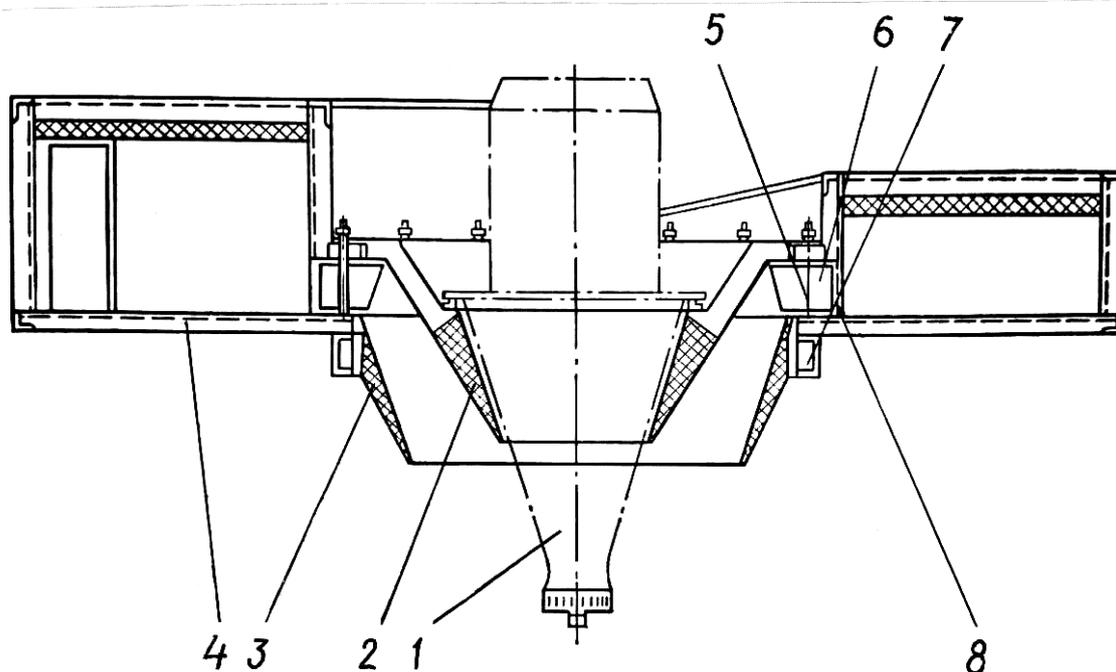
Воздухораспределитель: 1 – распылитель; 2 – внутренний конус; 3 – наружный конус; 4 – корпус; 5 – ось лопасти; 6 – лопасть; 7 – канал для охлаждающего воздуха; 8 – уравнивающая решетка.
